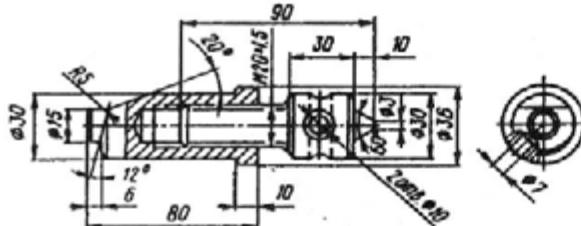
Приспособление для выпрессовки пальца шаровой опоры
